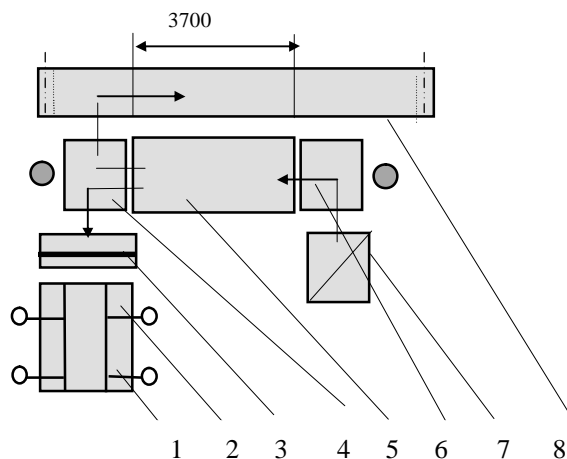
Схема организации рабочего места у станка ПРС-2: 1 - шпоноукладчик форматных листов, 2 - подъёмный стол, 3 - ножницы, 4 - приемный стол, 5 - прирезной-ребросклеивающий станок, 6 - загрузочный стол, 7 - стопа кускового шпона, 8 - конвейер возврата.
